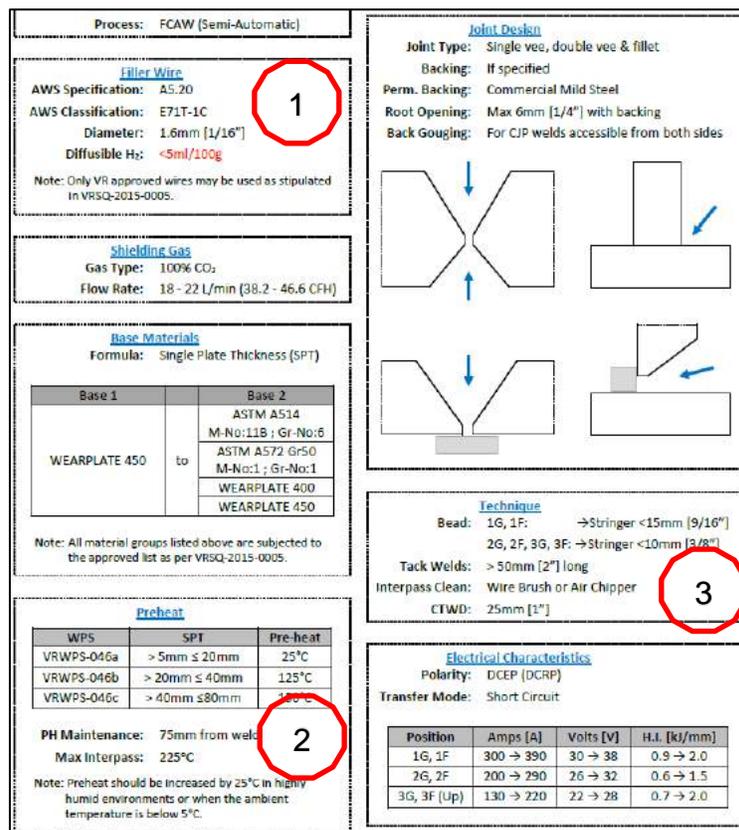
Procedimiento de soldadura (Welding Procedure)
